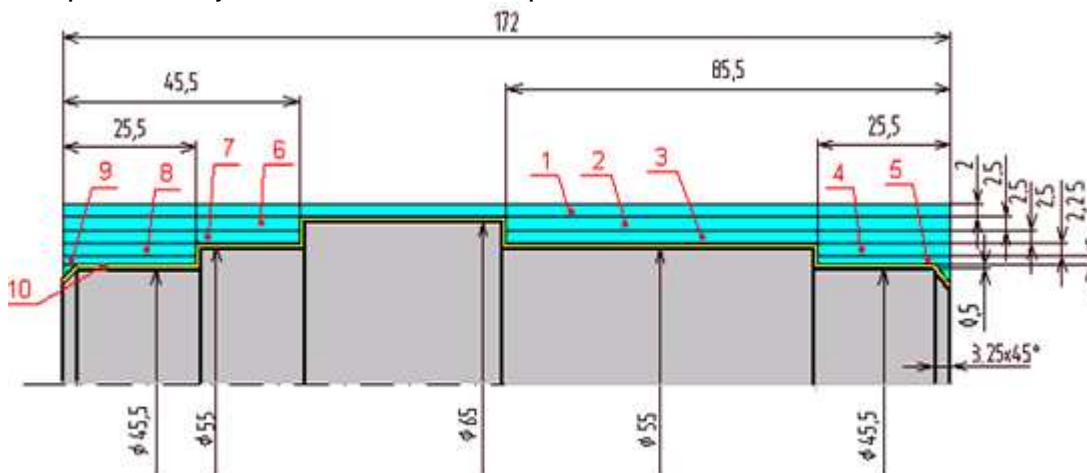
8 Obrábění zápichů na univerzálním stroji [13].
